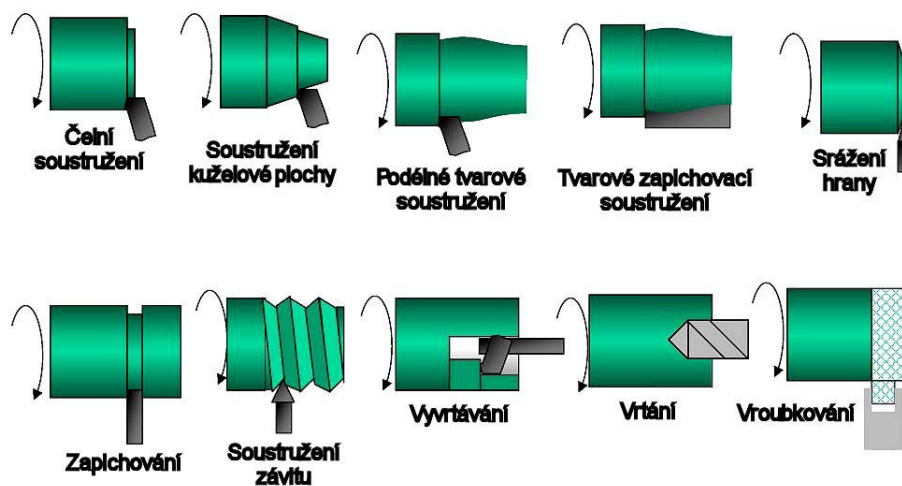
Soustružení na CNC stroji<sup>2</sup>
